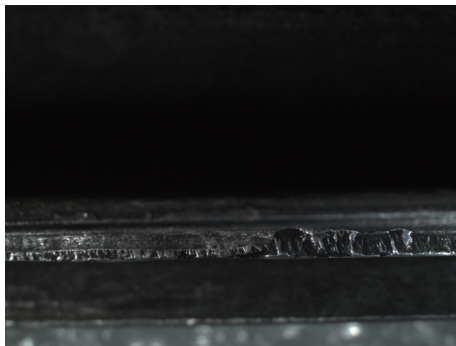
排气段隔板焊缝断口形貌 (10X)
